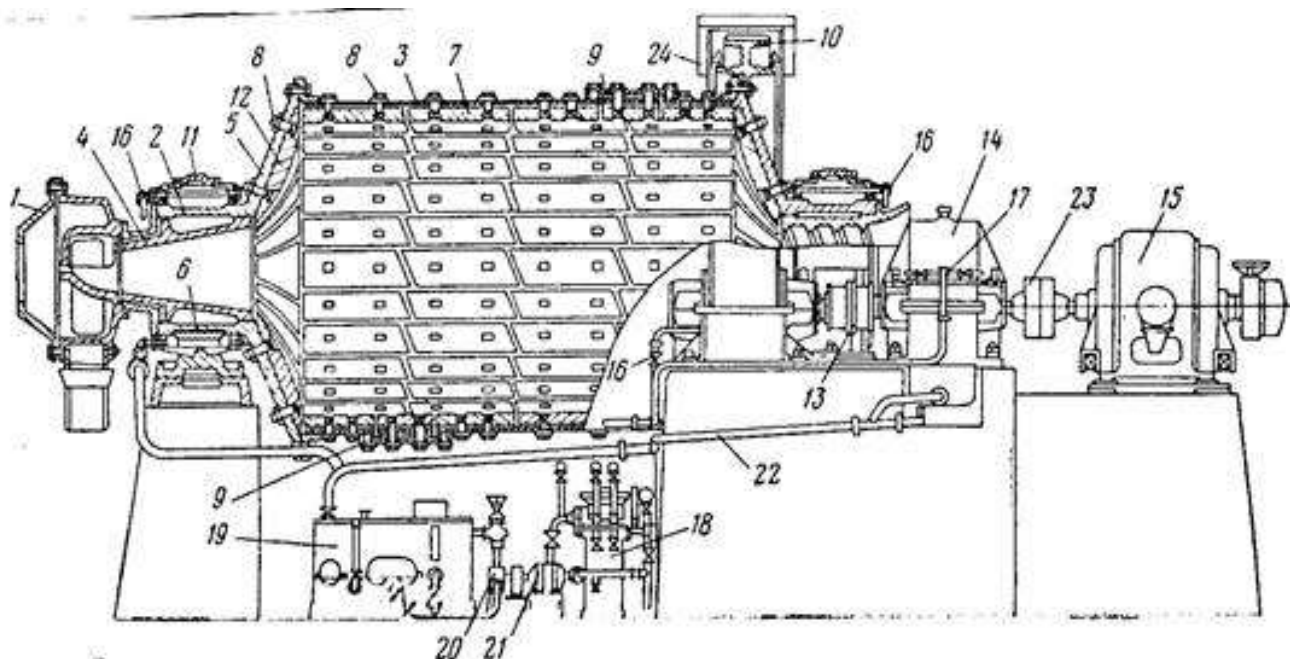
Кульовий млин МШЦ-2700x3600: 1 – живильник (комбінований); 2 – цапфи (горловини); 3 – барабан (обичайка); 4 - футерування-патрубок цапфи; 5 – кришки; 6 – корінний (головний) підшипник; 7 - футерування барабана; 8 - футерувальні болти; 9 – люки барабана; 10 - вінцева шестерня (зубчастий вінець); 11 – корпус підшипника; 12 - футерування кришки; 13 - муфта вал-шестірні; 14 – редуктор; 15 – головний електродвигун; 16 - нагнітальний оливопровід мастила млина; 17 - нагнітальний оливопровід редуктора; 18 - оливоохолоджувач; 19 - бак-відстійник; 20 - оливонасоси; 21 - двигун оливонасоса; 22 - зливний оливопровід; 23 - муфта головного двигуна; 24 - кожух вінцевої шестерні.
